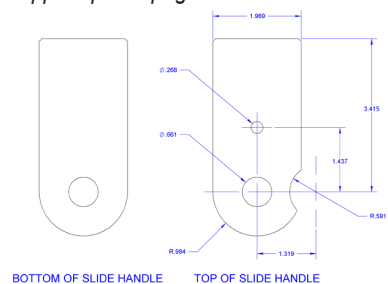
E2. Dimensioni di montaggio dell'impugnatura scorrevole.
